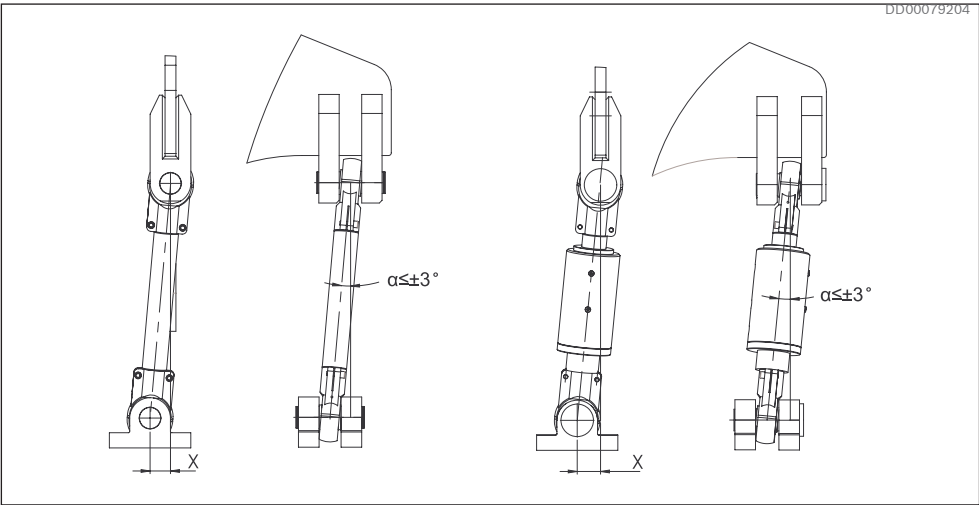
Montage von Gelenkverbindung und Hydraulikzylinder für DTCB
